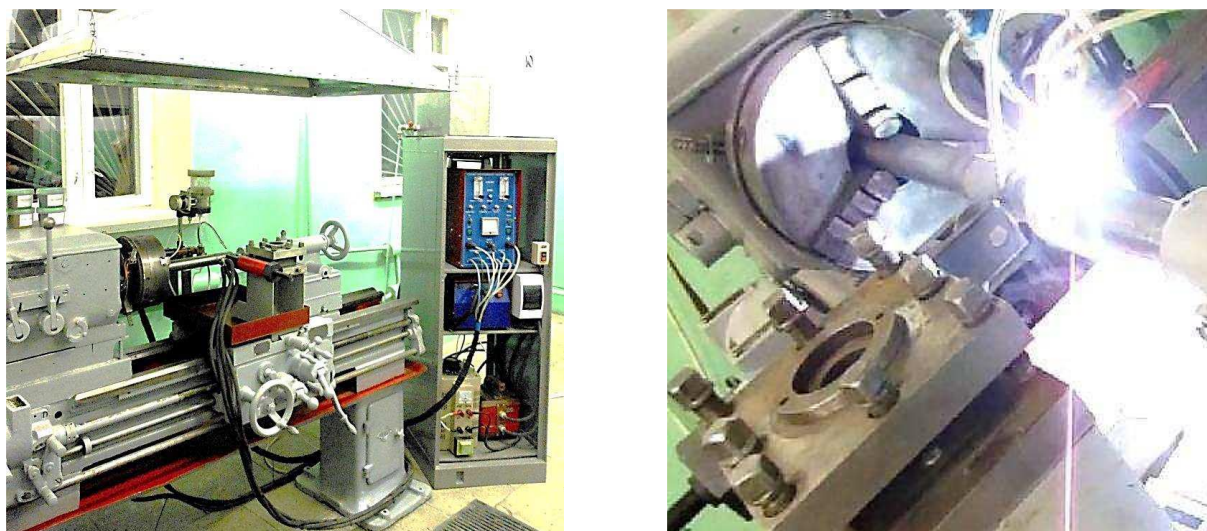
Комплектация модернизированной установки для плазменной наплавки
